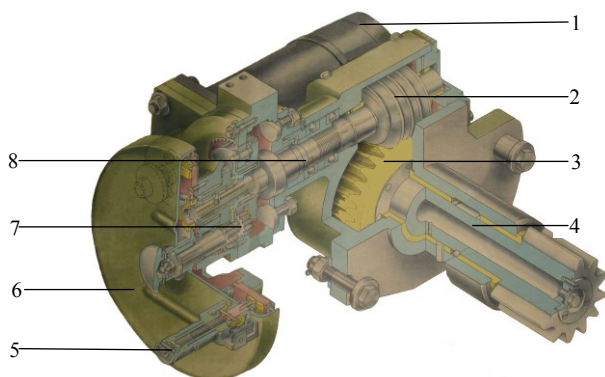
Піднімальний механізм СГ 2С3М: 1 – електродвигун; 2 – черв'ячний вал; 3 – черв'ячне колесо; 4 – вал із шестернею; 5 – рукоятка; 6 – маховик; 7 – блок-шестерні; 8 – хрестовина
